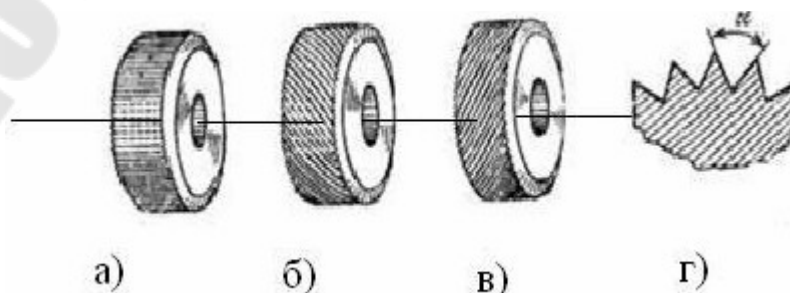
Ролики для накатки поверхностей: а – для прямой накатки; б – с левой насечкой; в – с правой насечкой; г – угол насечки
